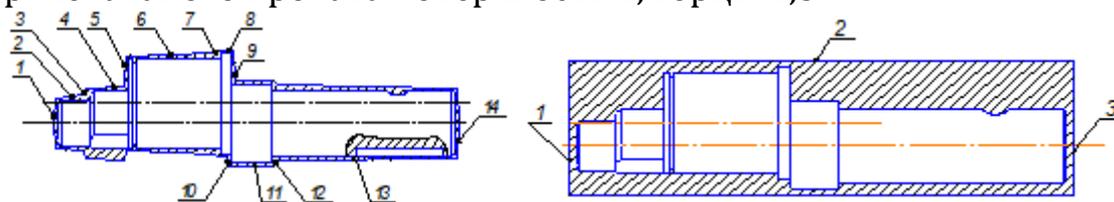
Эскиз заготовки детали «Вал»: а) поковка; б) прокат
